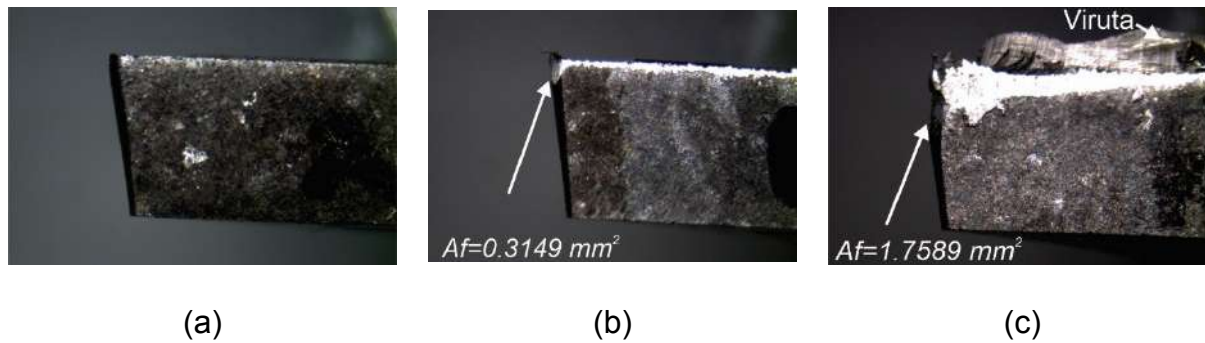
Estados de desgaste de la herramienta: (a) herramienta nueva, (b) herramienta desgastada y (c) herramienta rota.
